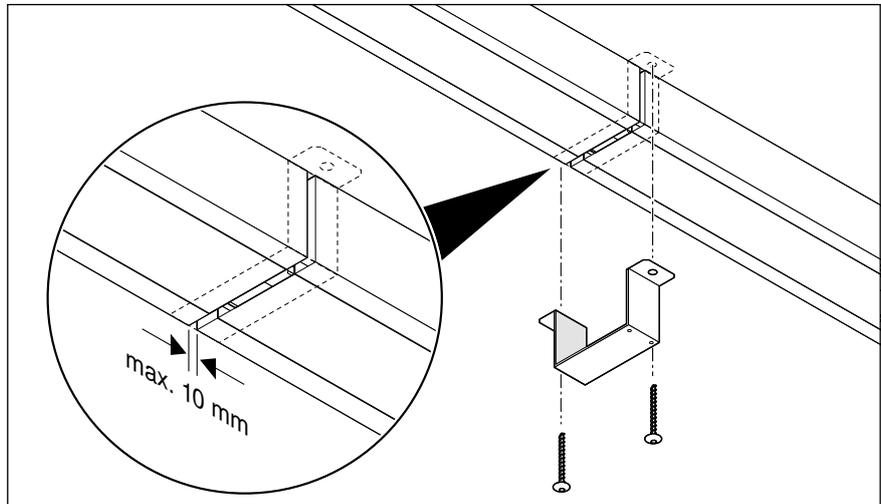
Kanalteilstücke mit Verbinder fixieren
